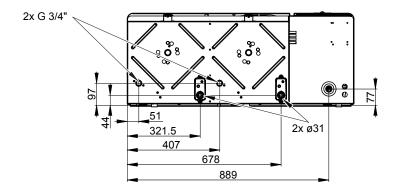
Dimensions Condair EL 50 - 90, taille de boîtier "L" (mesures en mm)
